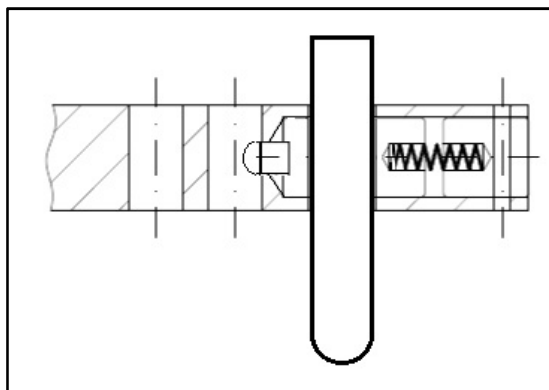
Suporte de tubos com mecanismo de fixação por mola.
